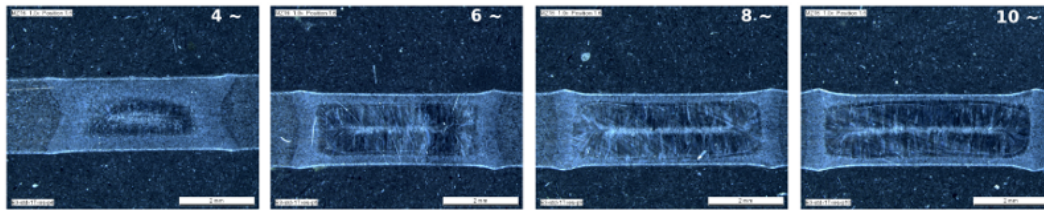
Cinétique expérimentale de développement du noyau - assemblage 1T XES 2mm - 100 points soudés paramètres standard.
